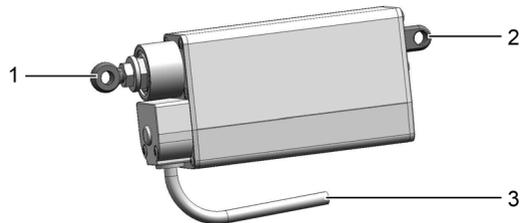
Linearantrieb Junior 0E mit Anschlusskabel
